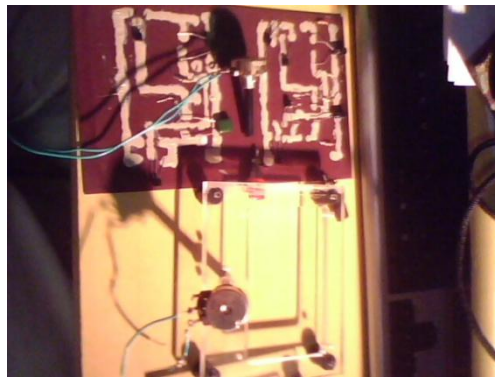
Placa corroída, componentes eletrônicos e base de acrílico para apresentação.
